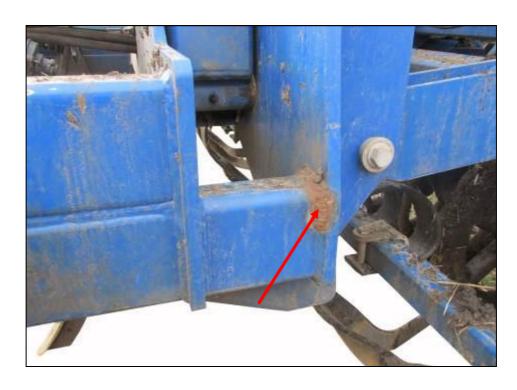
Сварка по месту разрыва (по сварному шву) центральной рамы
